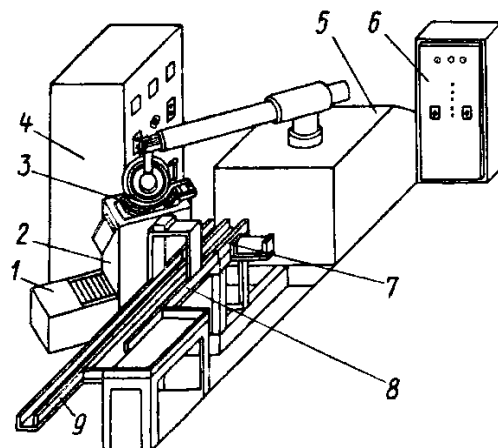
Типовая установка для ультразвуковой расконсервации подшипников.
